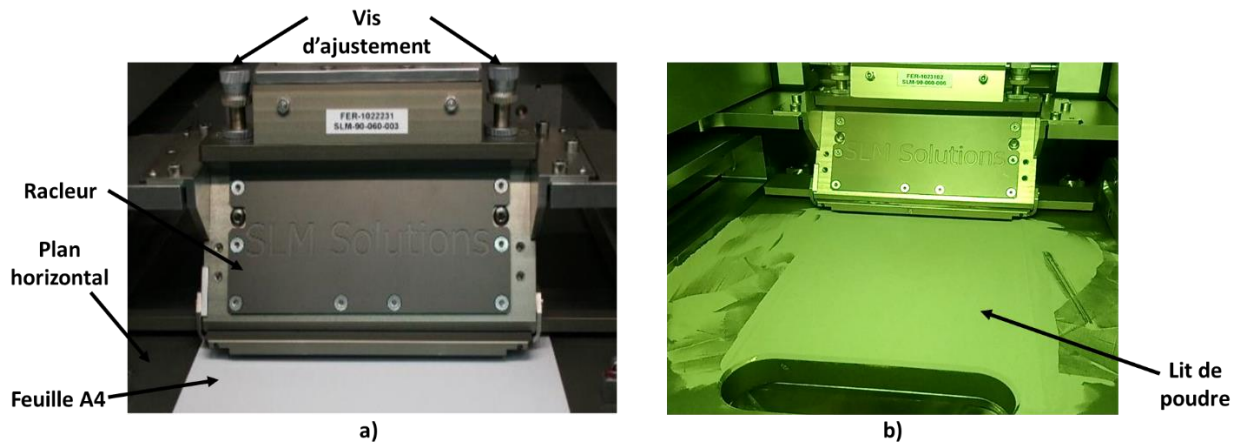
Préréglages de la chambre de fabrication sur la machine SLM125HL : a) Ajustement du niveau du racleur, b) Première couche déposée
